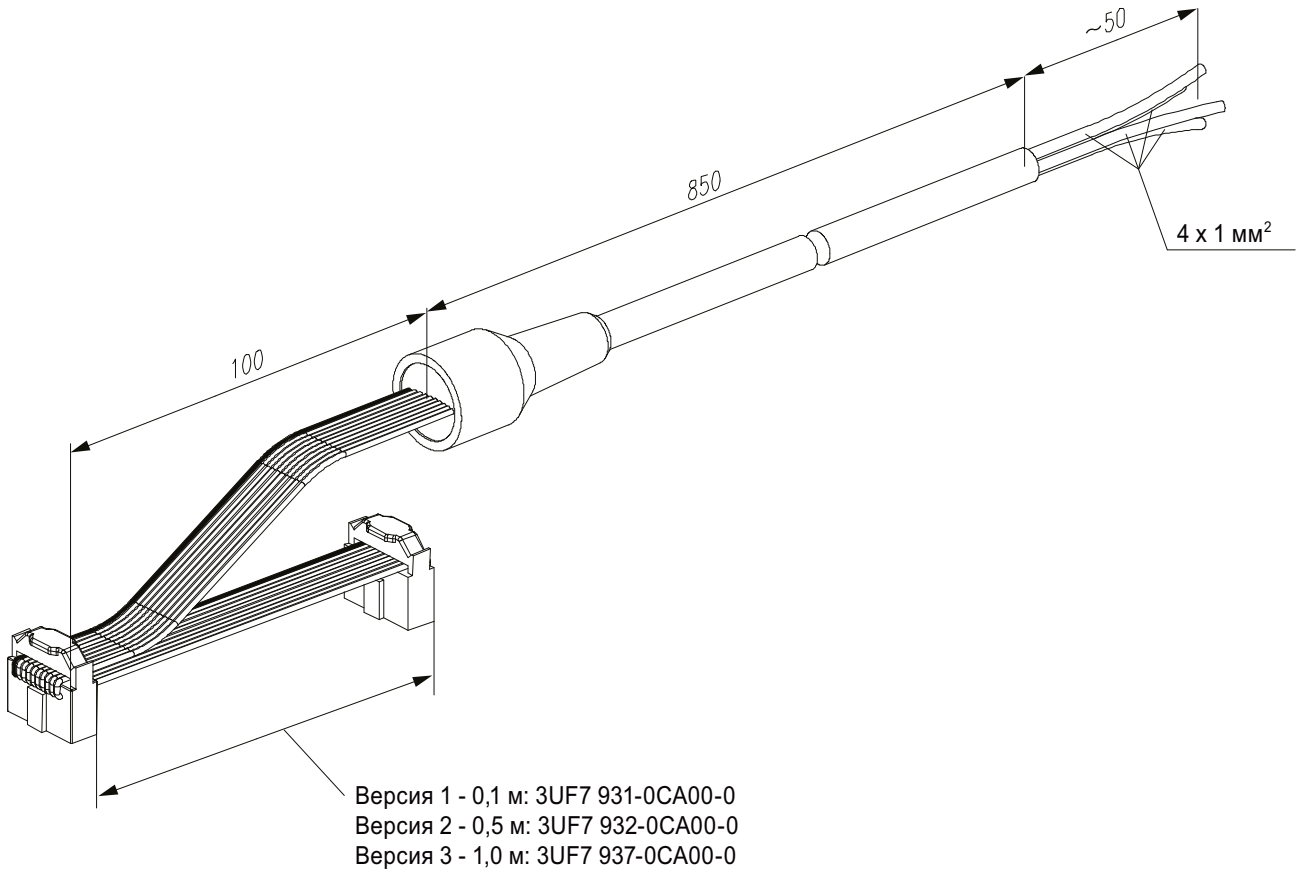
Габаритный чертеж Y-образного соединительного кабеля
